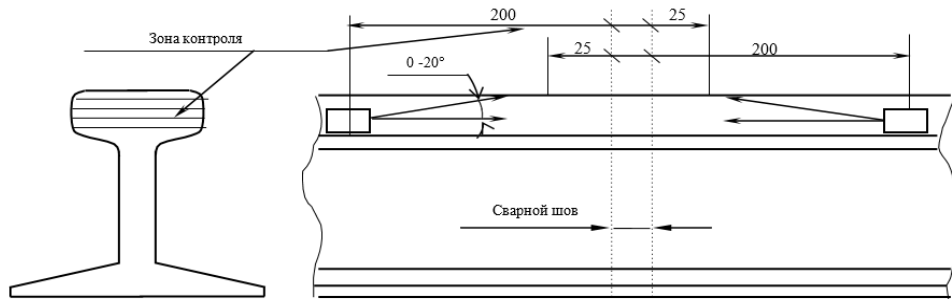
Контроль головки рельса с ее боковых поверхностей ПЭП с углом ввода 70°
